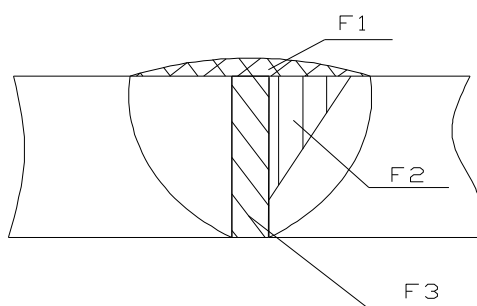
Схема расчета поперечной плоскости сварочного шва.
